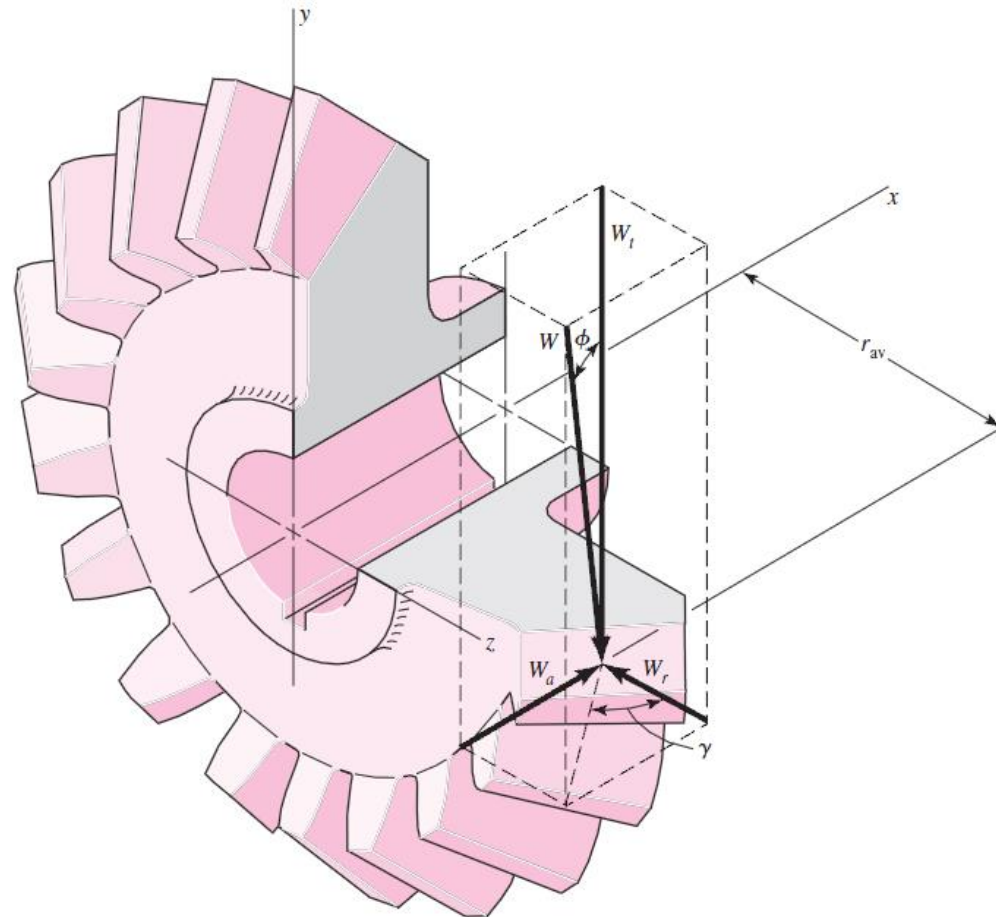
Forças atuando em engrenagens cônicas (Shigley, Mechanical Engineering Design, 2011)
